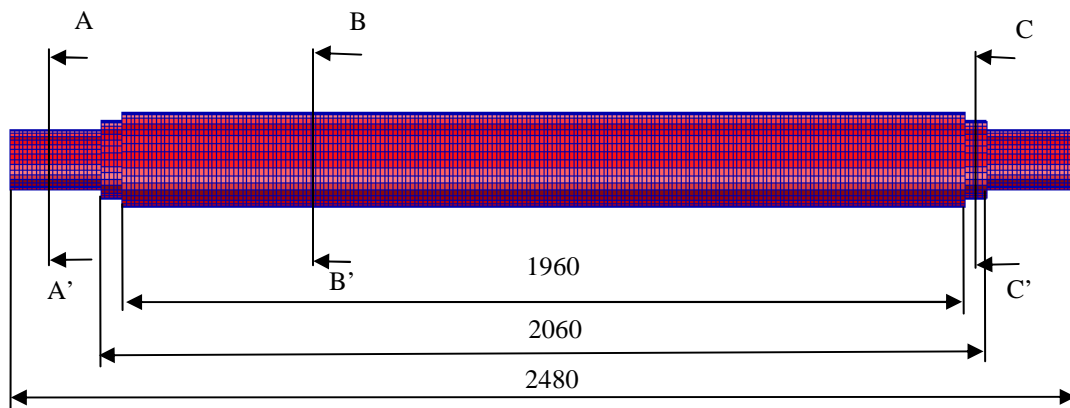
11: Dimensionado FEM componente principal (GFEM).
